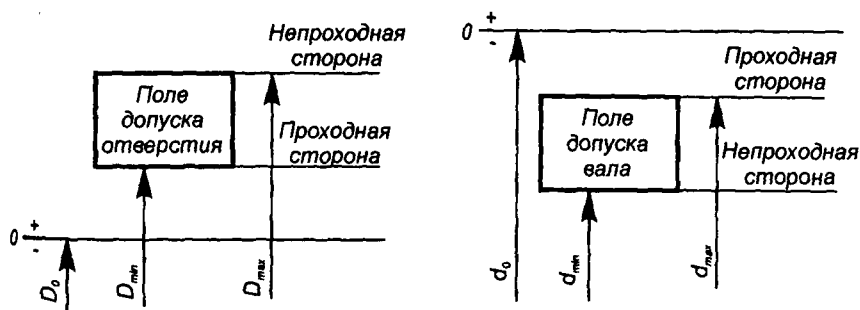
Схема определения номинальных размеров проходных и непроходных калибров.
